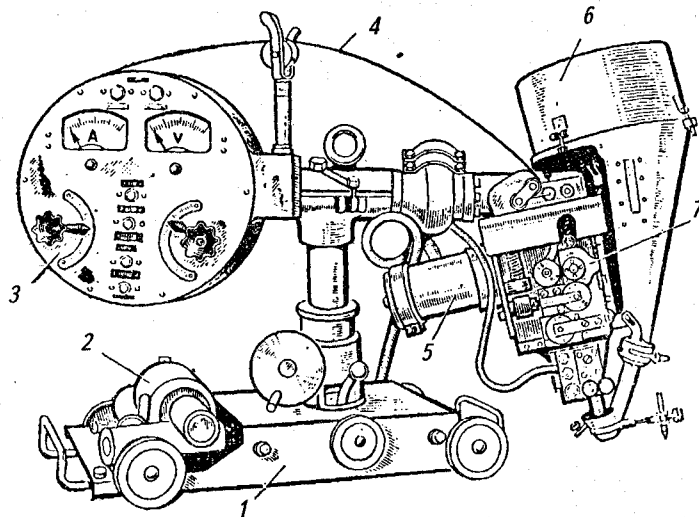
Сварочный трактор АДС-1000-2: 1 — самоходная каретка; 2 — электродвигатель для передвижения автомата; 3 — пульт управления с кассетой для проволоки; 4 — электродная проволока; 5 — электродвигатель механизма подачи проволоки; 6 — бункер для флюса; 7 — механизм подачи проволоки
